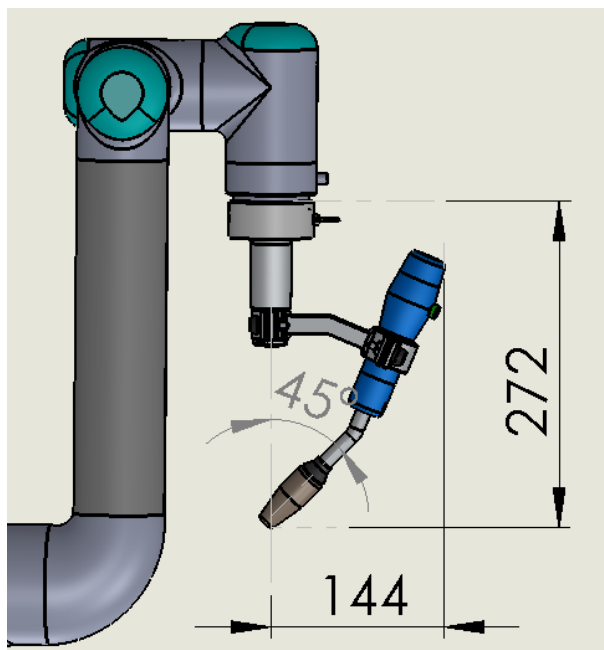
Dimensiones de la pistola de soldadura acoplada en el robot
